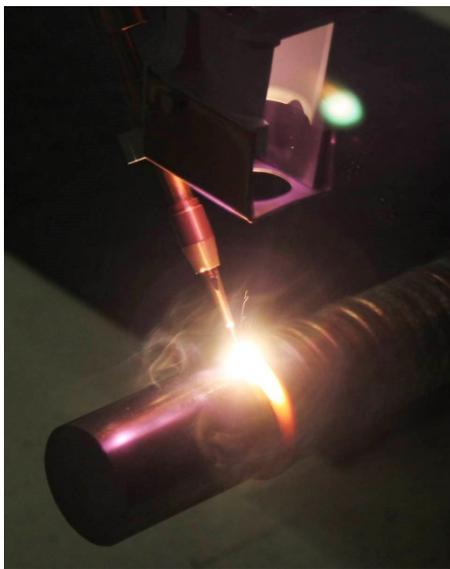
Beschichtung von S235 Rundmaterial mit Inconel625 durch Laser-Drahtauftragschweißen (Quelle: Fraunhofer IWS)
